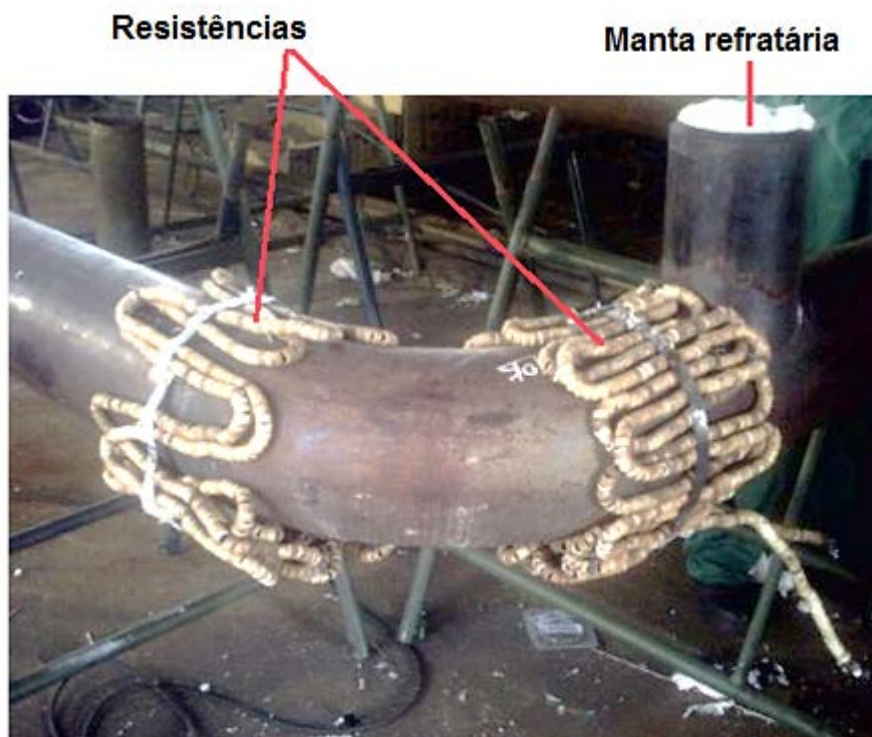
Resistências utilizadas para controle da soldagem – pré-aquecimento, interpasse e pós-aquecimento – (figura extraída da internet – Advel tecnologia) mar-2013.
